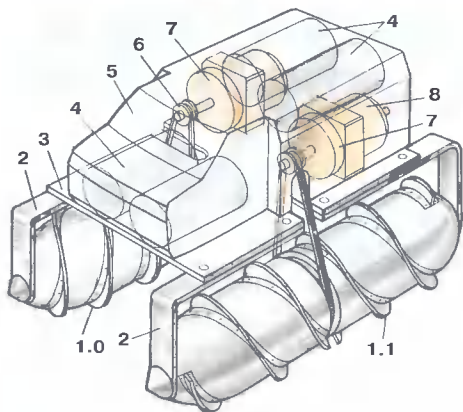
Компоновка шнекохода с двумя реверсивными электродвигателями: 1.0 — правый шнек; 1.1 — левый шнек; 2 — кронштейн (4 шт.); 3 — платформа; 4 — батарея питания; 5 — кузов; 6 — ременная передача (2 шт.); 7 — редуктор двигателя (2 шт.); 8 — электродвигатель (2 шт.).
